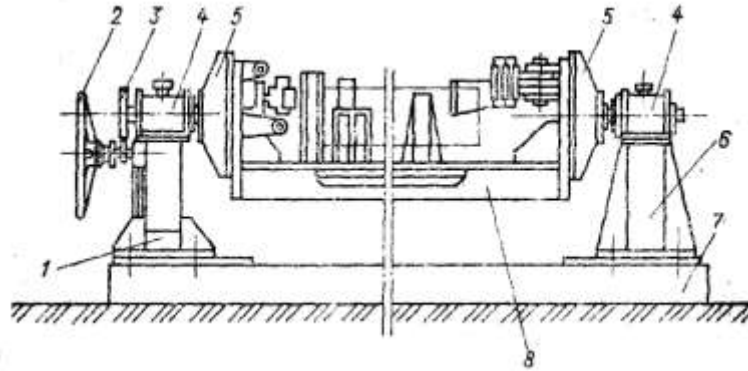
Кондуктор-кантователь для сборки элементов фонарей
